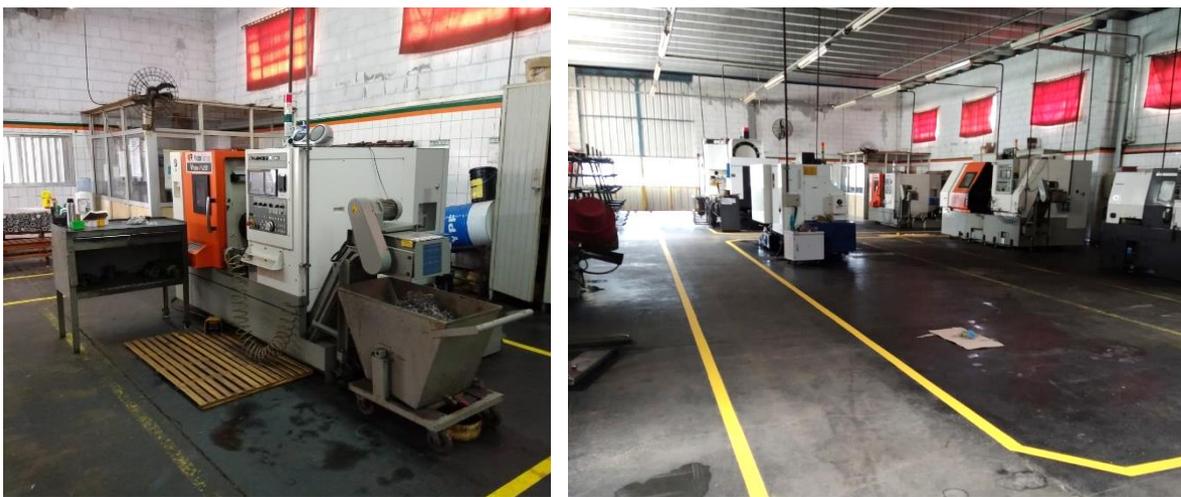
Torno CNC "Víctor" (izquierda) y sector de mecanizado (derecha).
